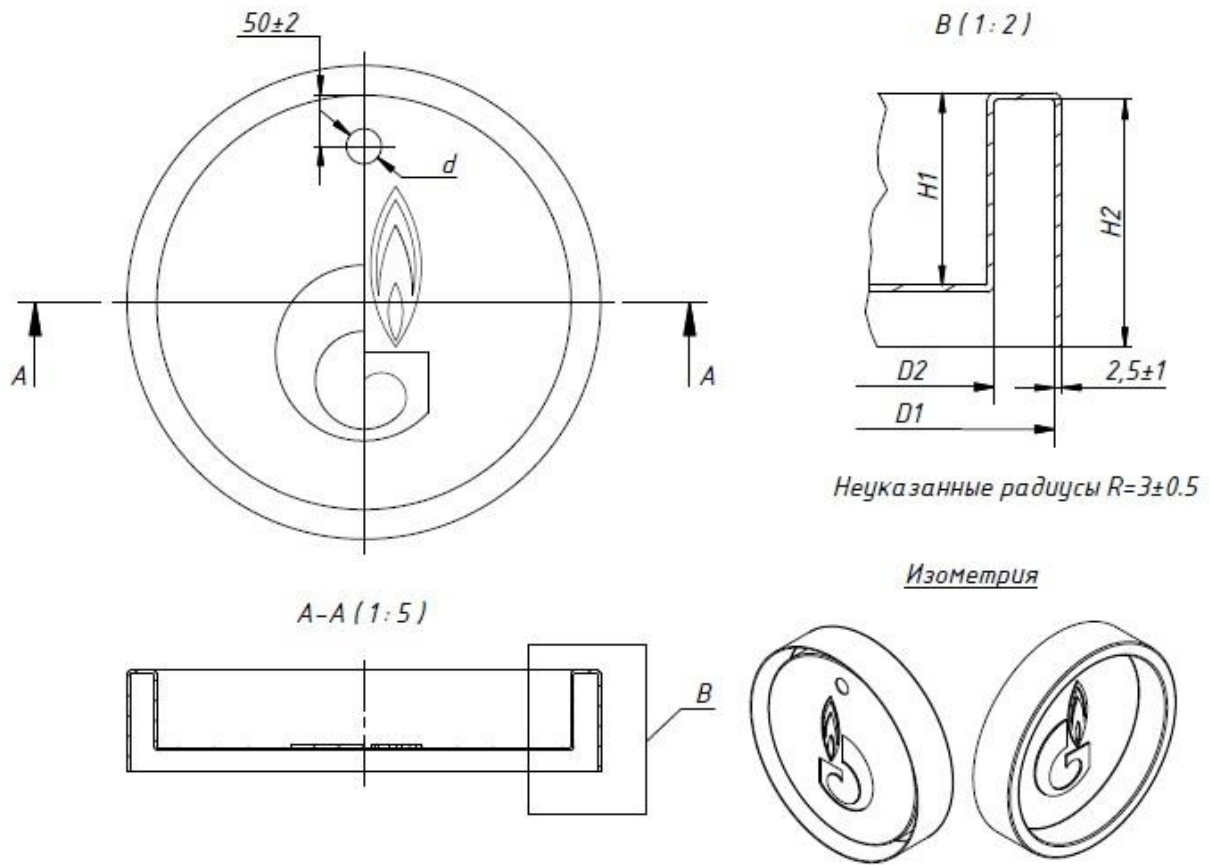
Стандартная конструкция и размеры полимерных заглушек
